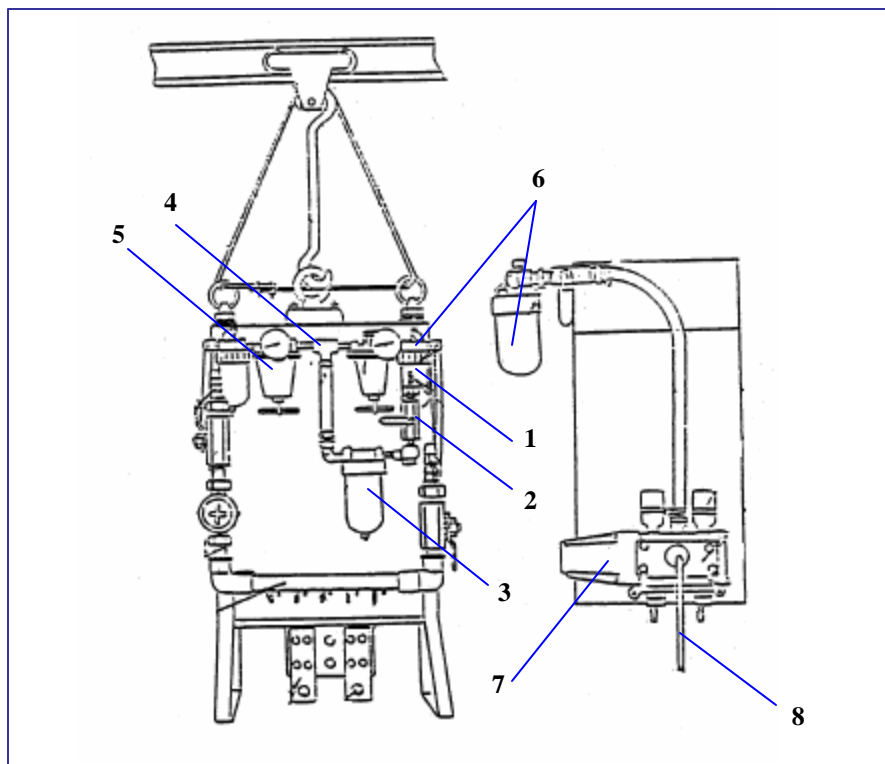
Partes del sistema neumático de un equipo soldador de puntos
